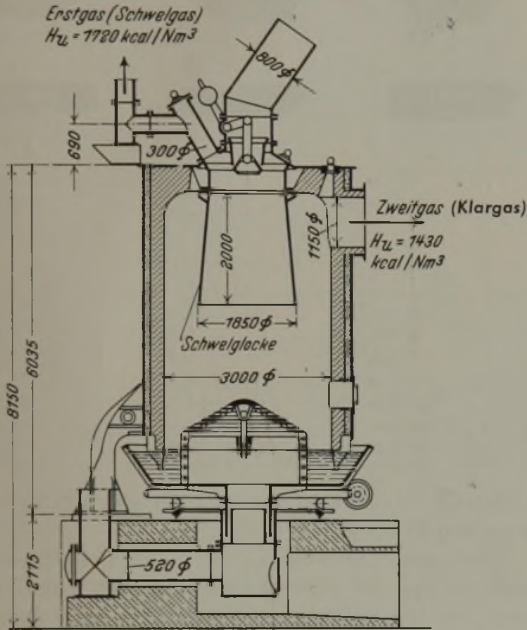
3-m-Gaserzeuger mit eingebauter Schwelglocke.
